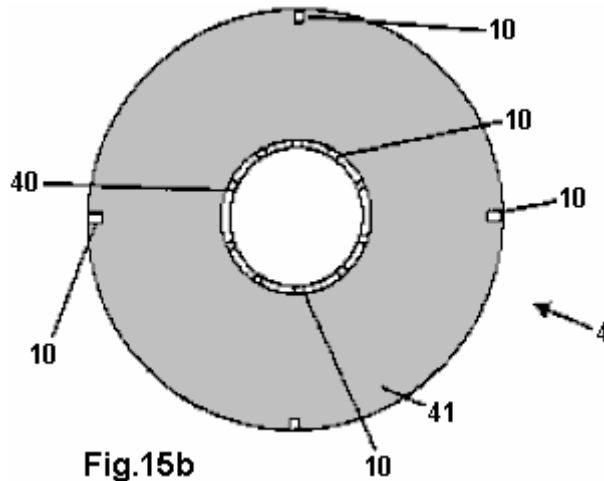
zeigt die Befestigungsvorrichtung 4 in einer Ansicht in Richtung der Wellenachse 50. Der Montagering Platte 41 weist an seinen Umfang vier Schrauben 10 zur Befestigung an dem mechanischen Gehäuse des Hohlzylinders 40, der an seinem Umfang eine Anzahl von Schrauben 10 zur Befestigung der inneren Stator anstelle.
